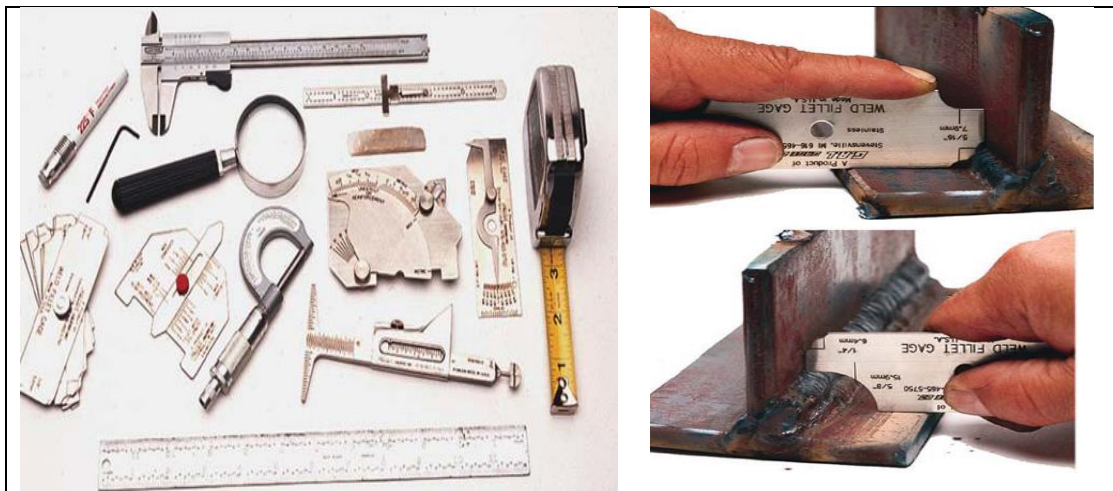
Equipamentos utilizados na inspecção visual de soldaduras.
